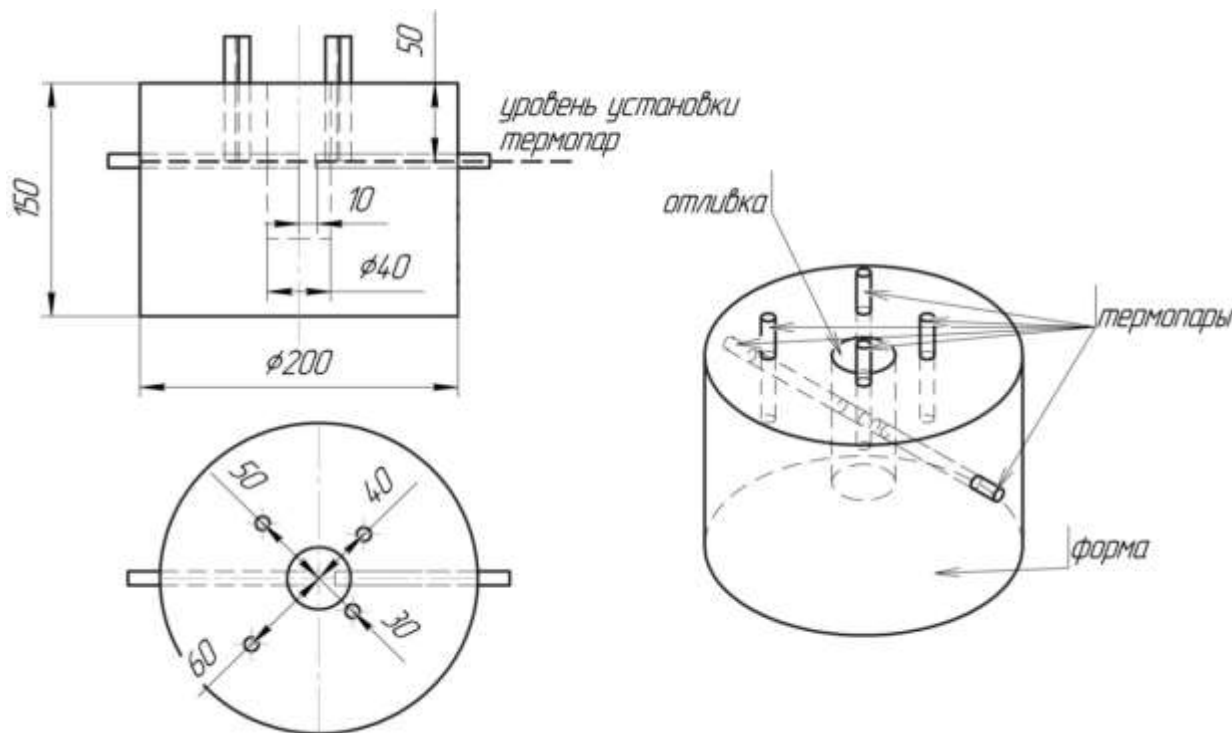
Схема расположения термопар в эксперименте по затвердеванию отливки в цилиндрической форме
